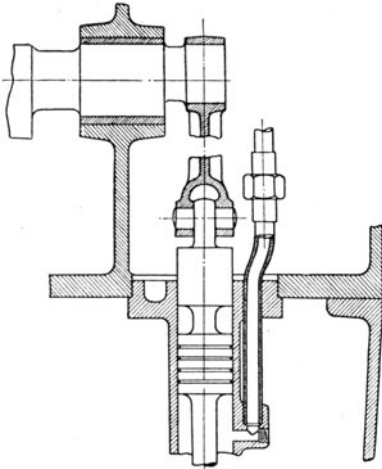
Gewöhnliche Kolbensmierschmierpumpen mit Saug- und Druckventil.
